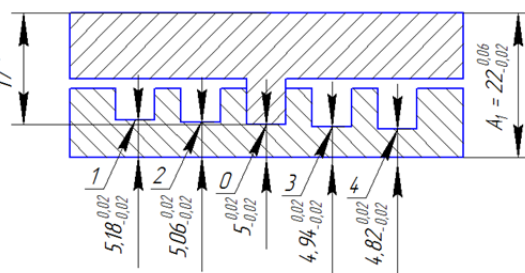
Развертка конструкции компенсатора со ступенями компенсации
